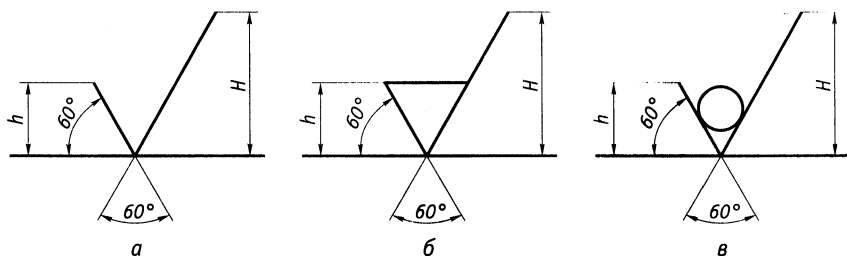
Обозначение шероховатости поверхностей, полученных разными способами обработки:
